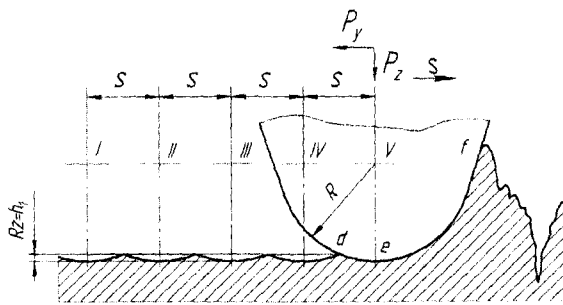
Кинематическая модель обработки торцевой поверхности заготовки
